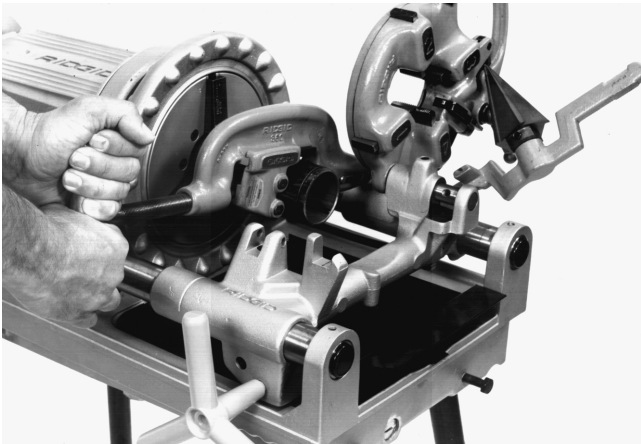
Corte de un tubo con la máquina Roscadora Compacta No. 300
